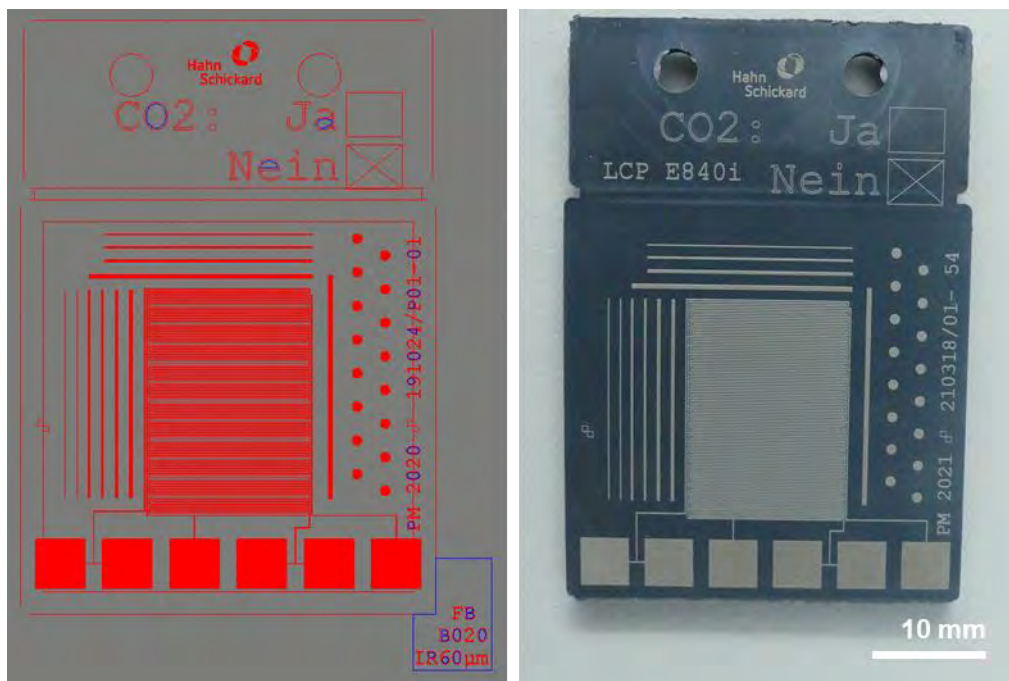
Angepasstes Testlayout und Lichtbildaufnahme einer damit gelaserten Probe.
